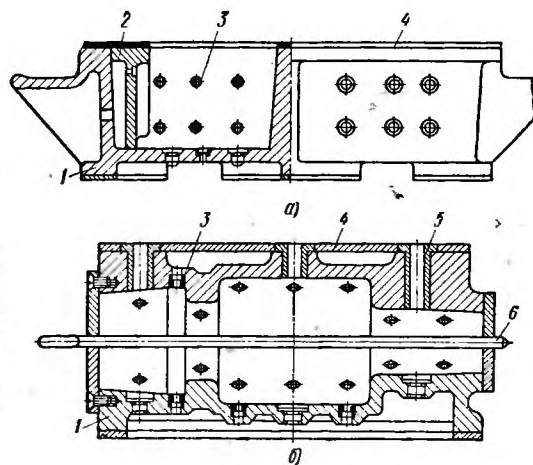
Ящики для пескодувных машин; а — открытый встряхной; б — закрытый с горизонтальным разъемом; 1 — корпус ящика; 2 — вкладыш; 3 — венты; 4 — армровка ящика; 5 — дувная втулка; 6 — душник
